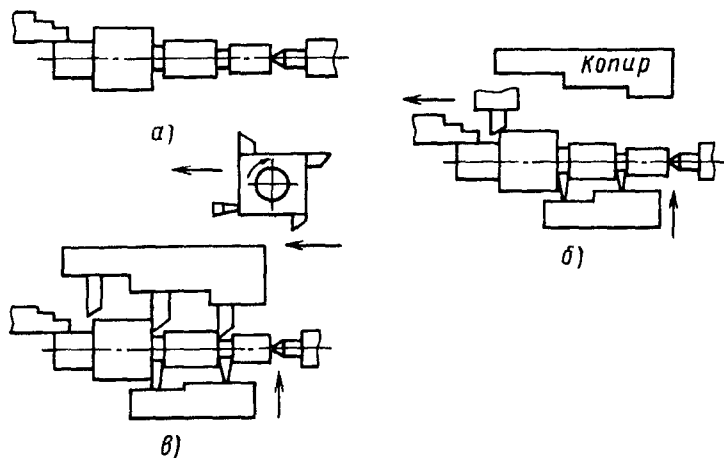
Схемы обработки заготовки ступенчатого вала точением:
